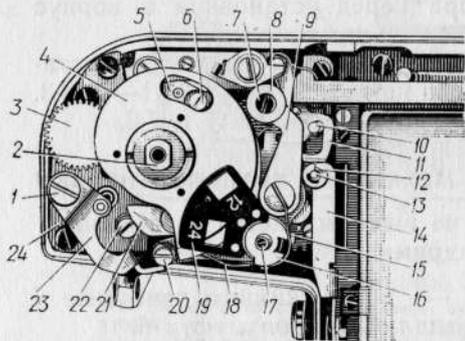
Механизм транспортировки без шкалы счетчика кадров в корпусе:
